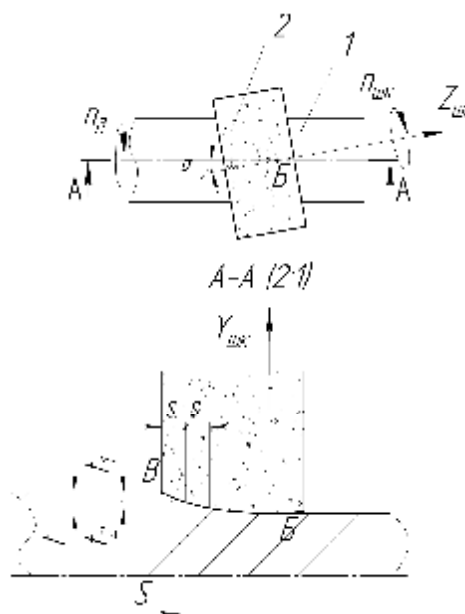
Шліфування широким циліндричним кругом зі схрещеними осями інструмента та деталі
